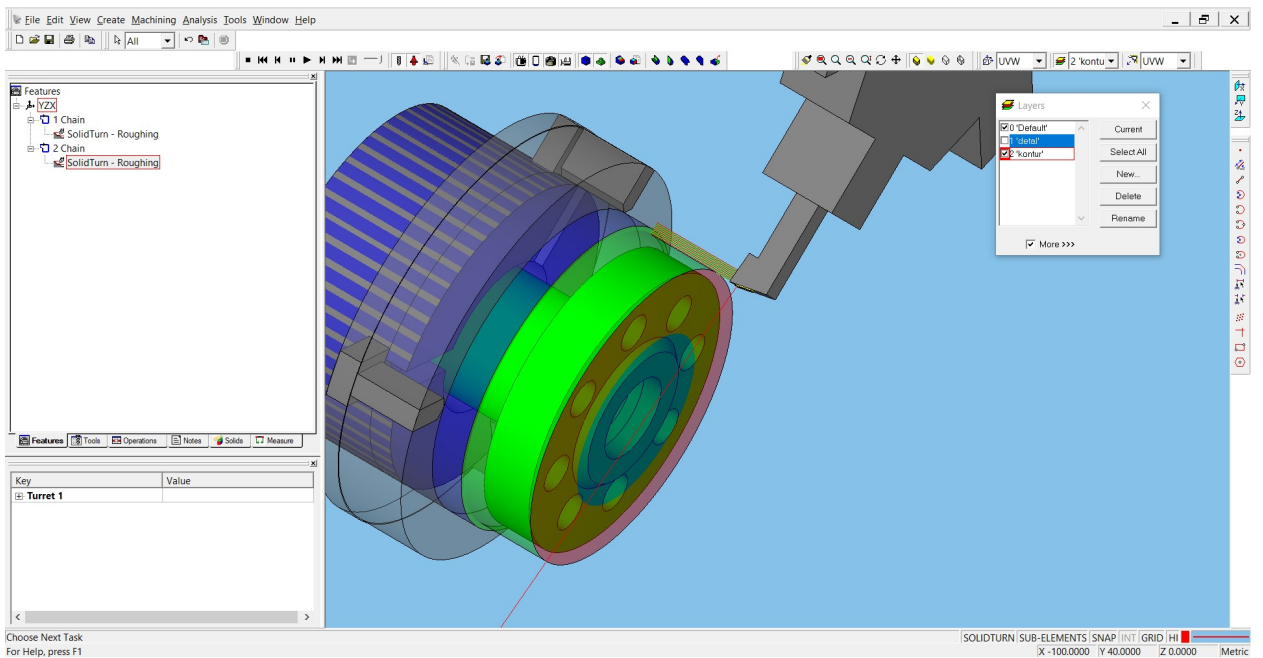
Траєкторія руху металорізального інструменту при обробленні кришки
